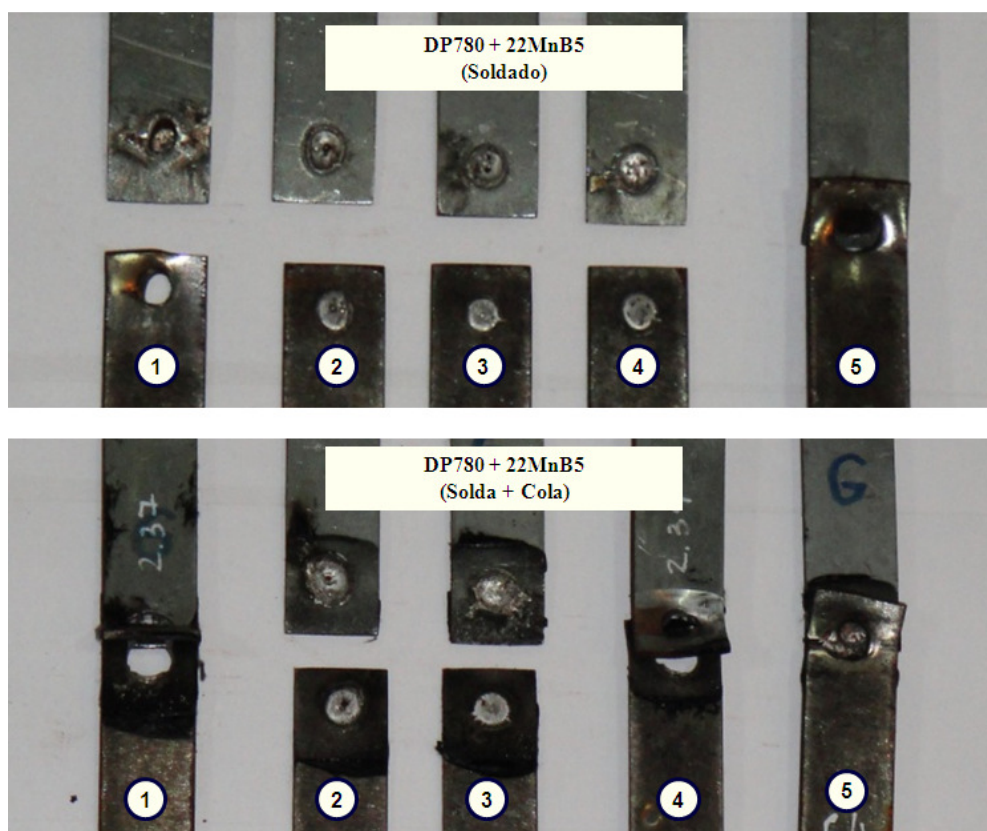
Detalhe das uniões soldadas rompidas DP780 + 22MnB5.
